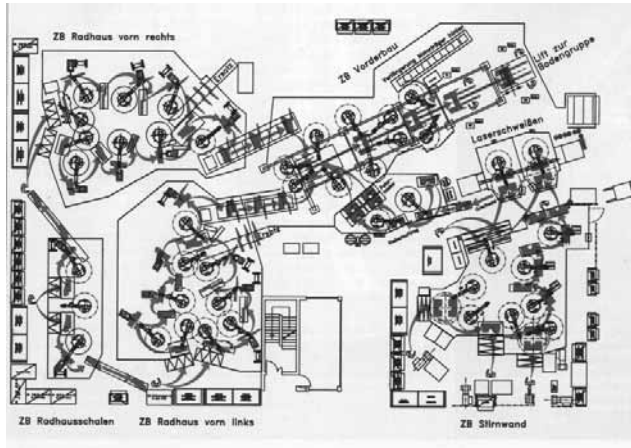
Layout eines Zusammenbaus (Ausschnitt) am Beispiel des BMW 5er, Dingolfing¹⁰⁰
